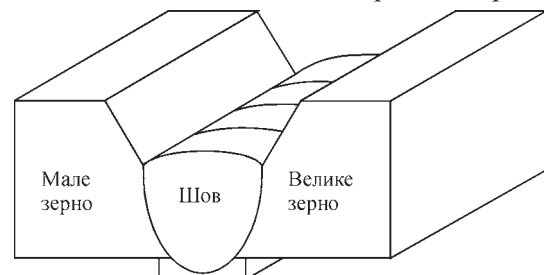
Схема зварного з'єднання з різним розміром зерен
